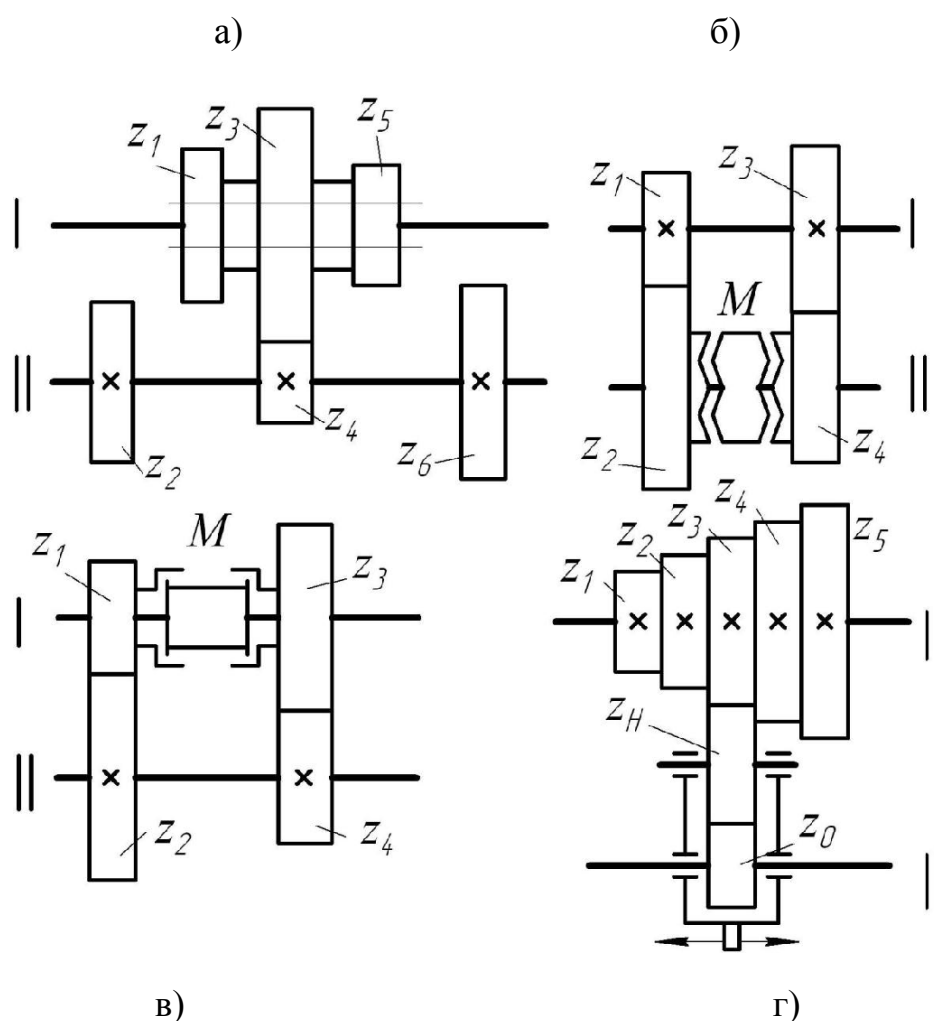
Схеми передач руху в коробках швидкостей
